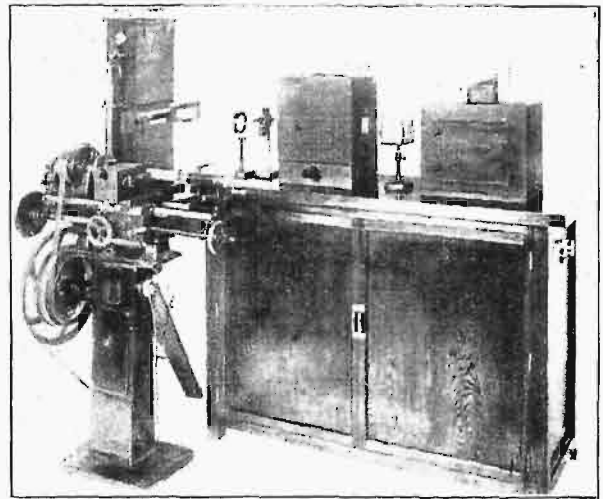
zapoznaje nas z wyglądem aparatu po zdjęciu zaś pokrywy. Rys. 4 przedstawia całość instalacji, składającej się z tokarki z napędem elektrycznym i aparatury rejestracyjnej.
